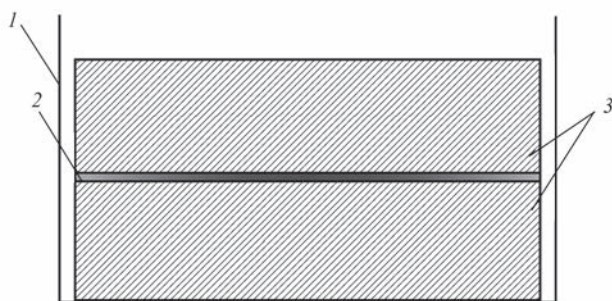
Схема поперечного перерізу шихтової заготовки: 1 — невитратний короб; 2 — шар порошку TiO_2 ; 3 — шихтова заготовка
